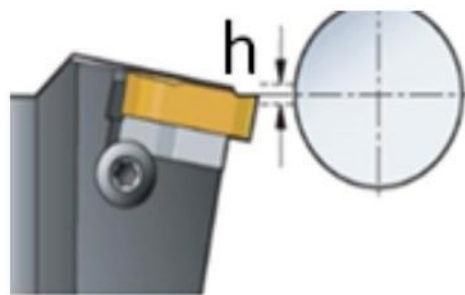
Схема установки вершини токарного різця із тангенціальним відхиленням його вершини h
